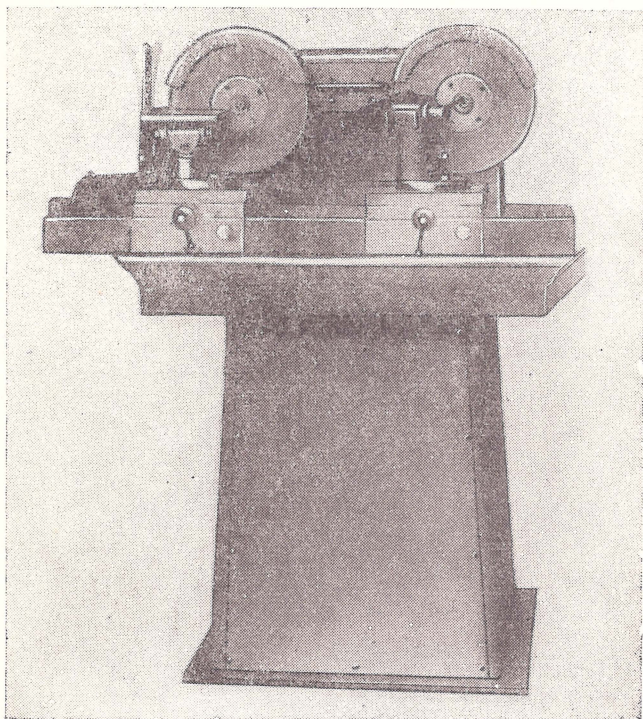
Доводочный полуавтоматический двухшпиндельный станок
